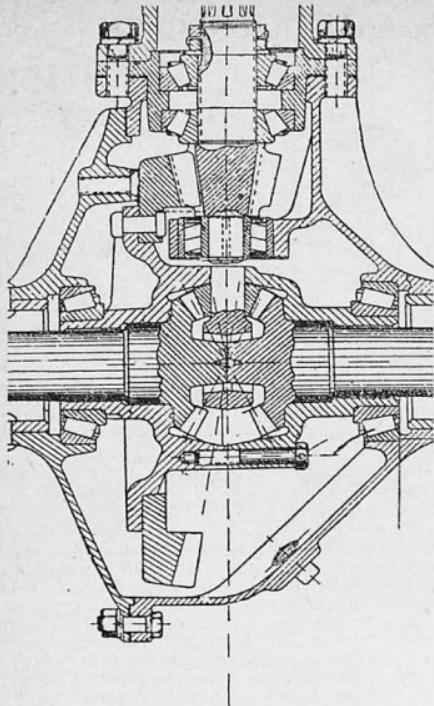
Установка подшипников ведомой шестерни на картере дифференциала
